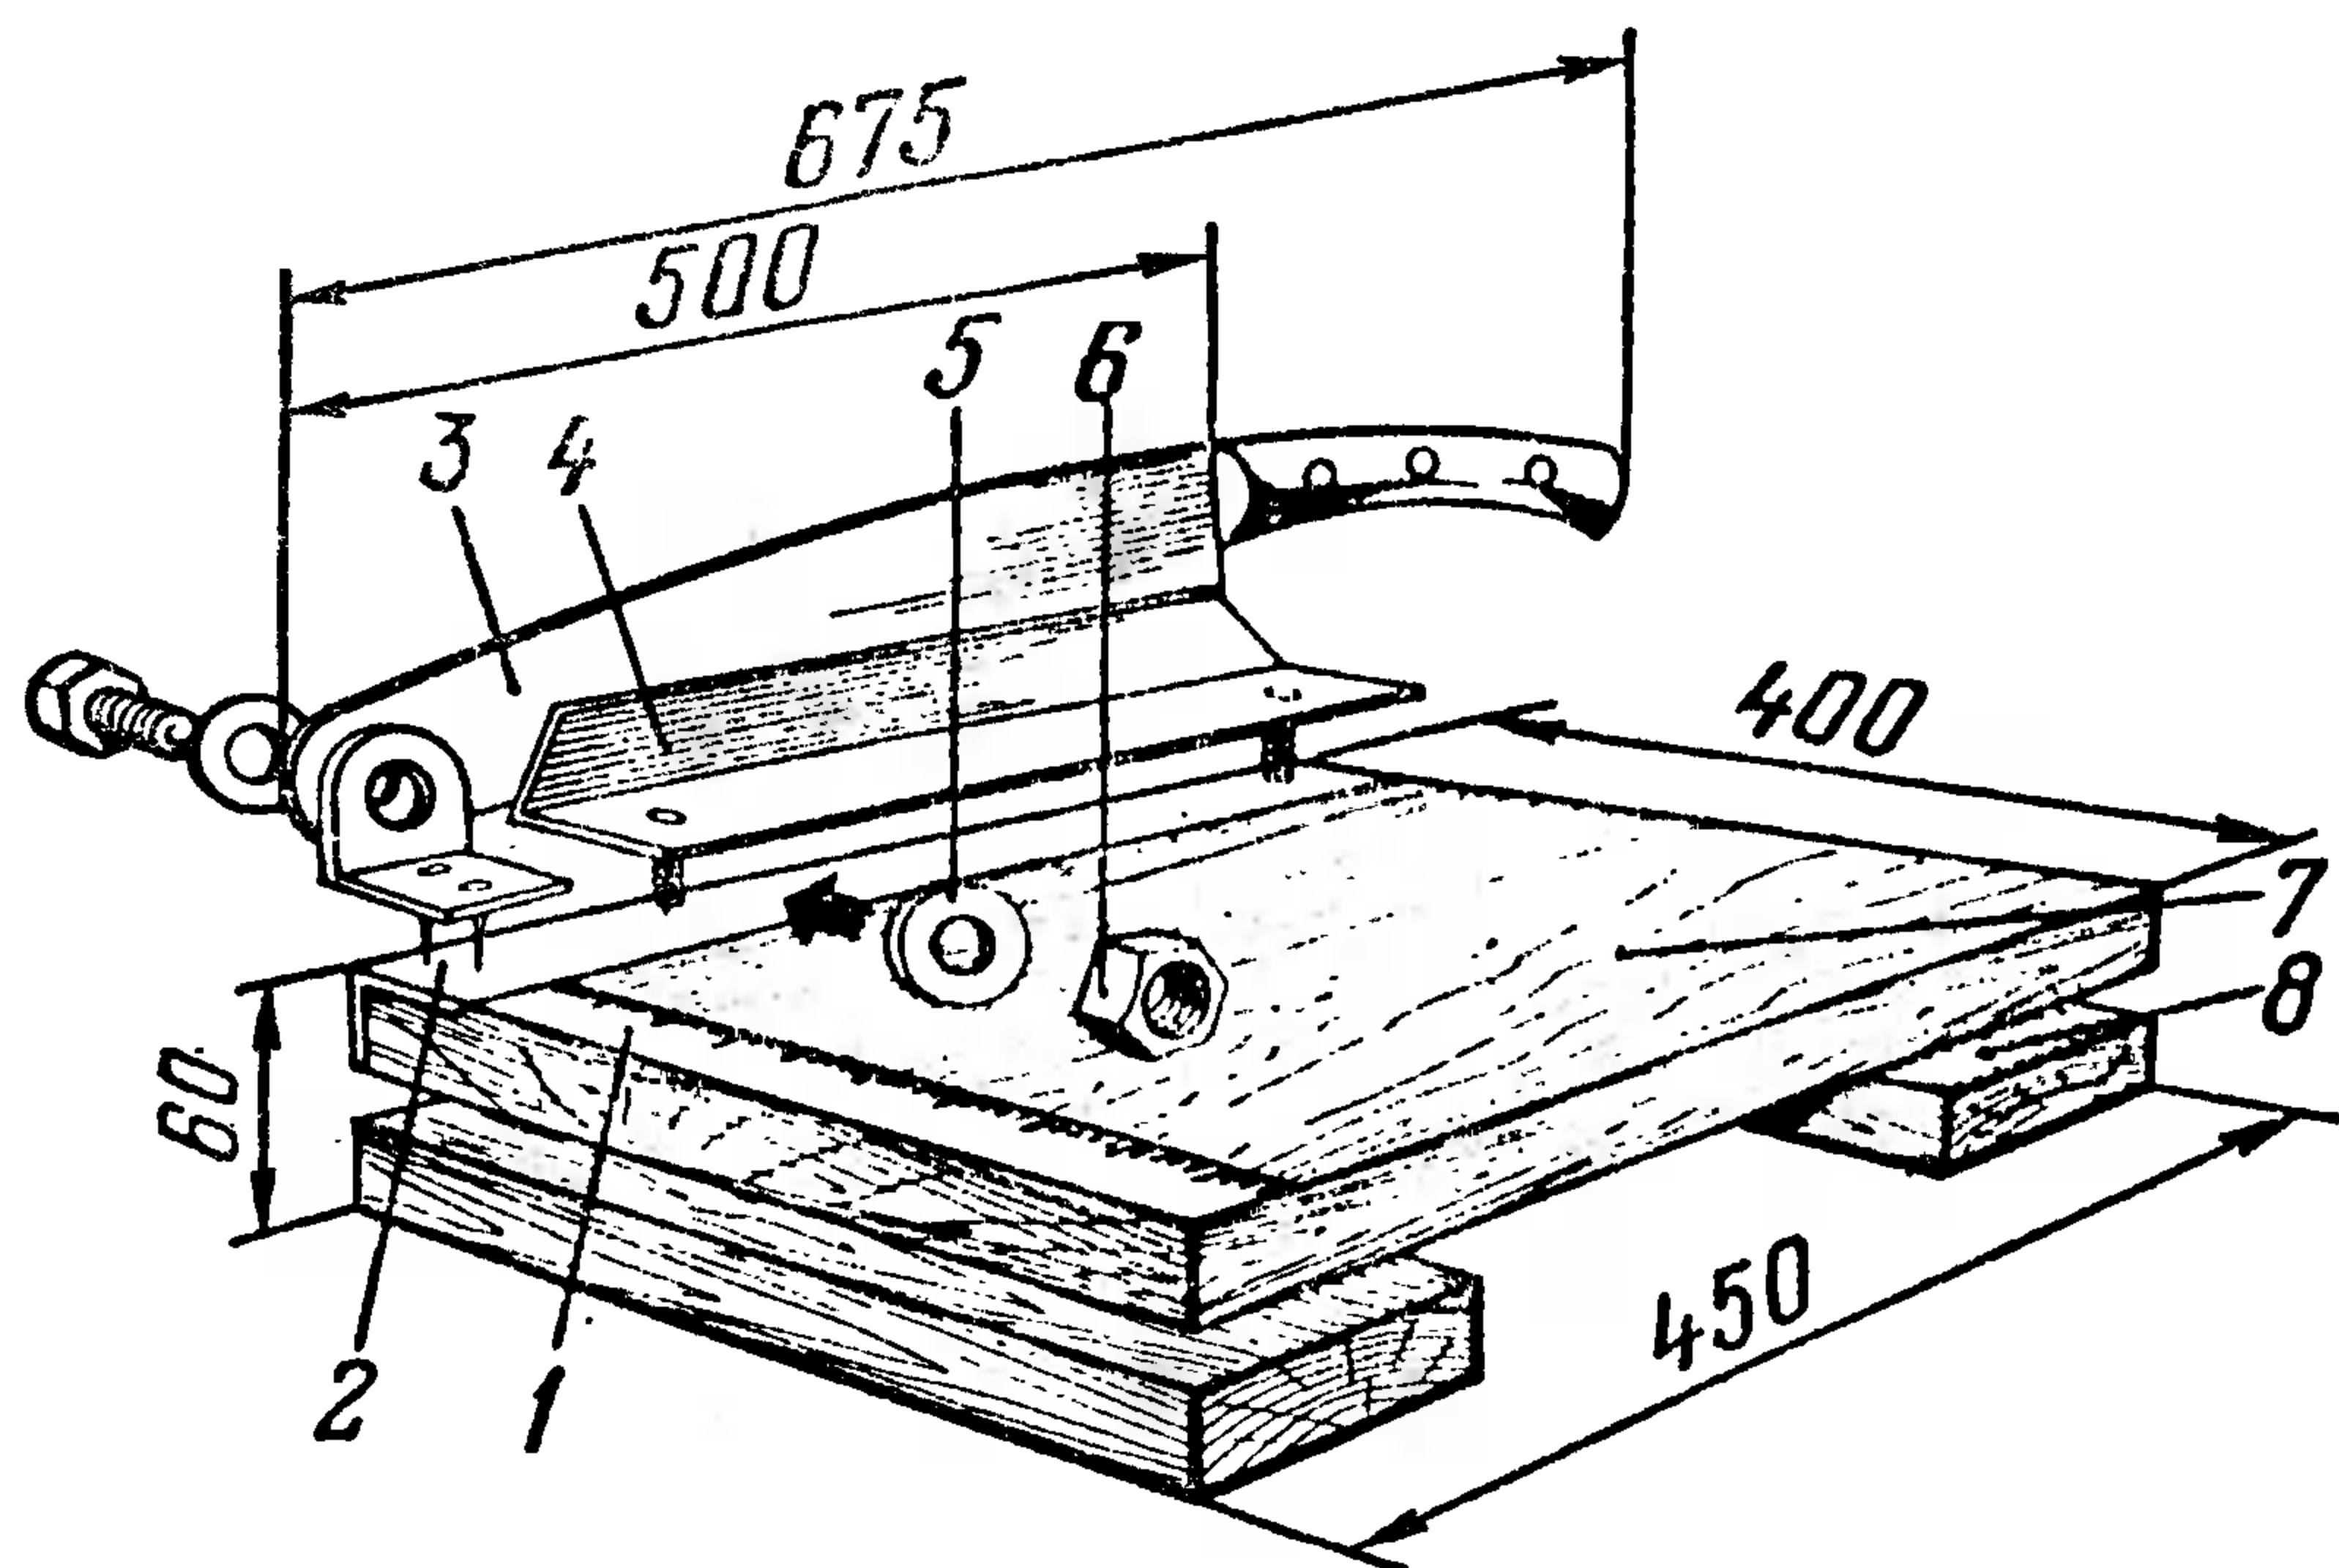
Картонорубилка: 1 — линейка; 2 — металлическая накладка (уголок); 3 — нож с рукояткой; 4 — прижимная планка; 5 — шайба; 6 — гайка; 7 — основание; 8 — опорные планки.
